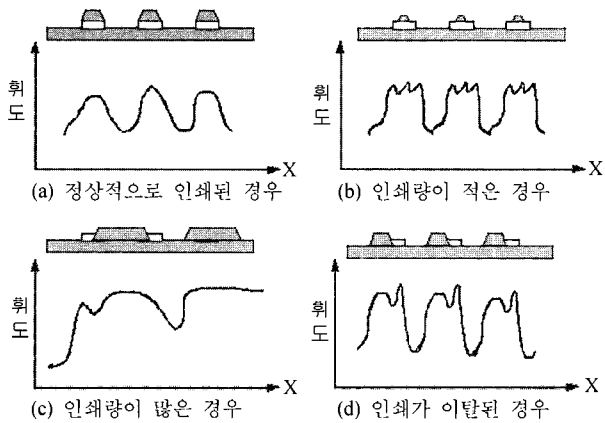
Solder Paste의 인쇄상태와 영상의 휘도 분포와의 관계.
